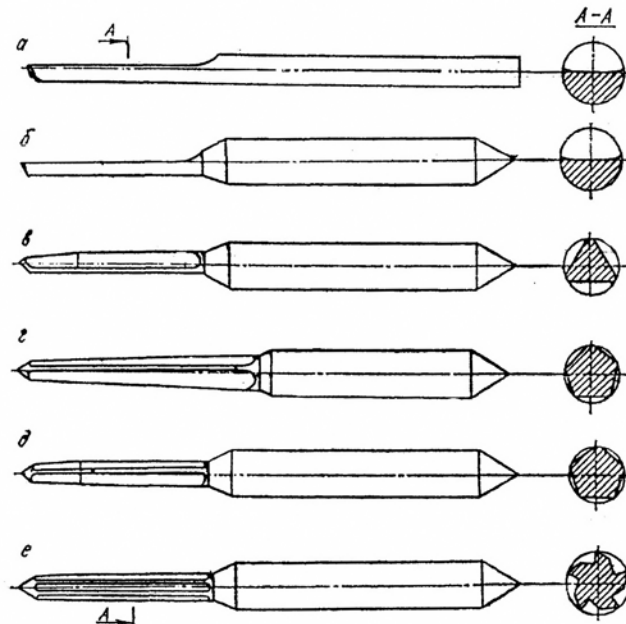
Развертки для обработки отверстий диаметром 0,1—3 мм:
